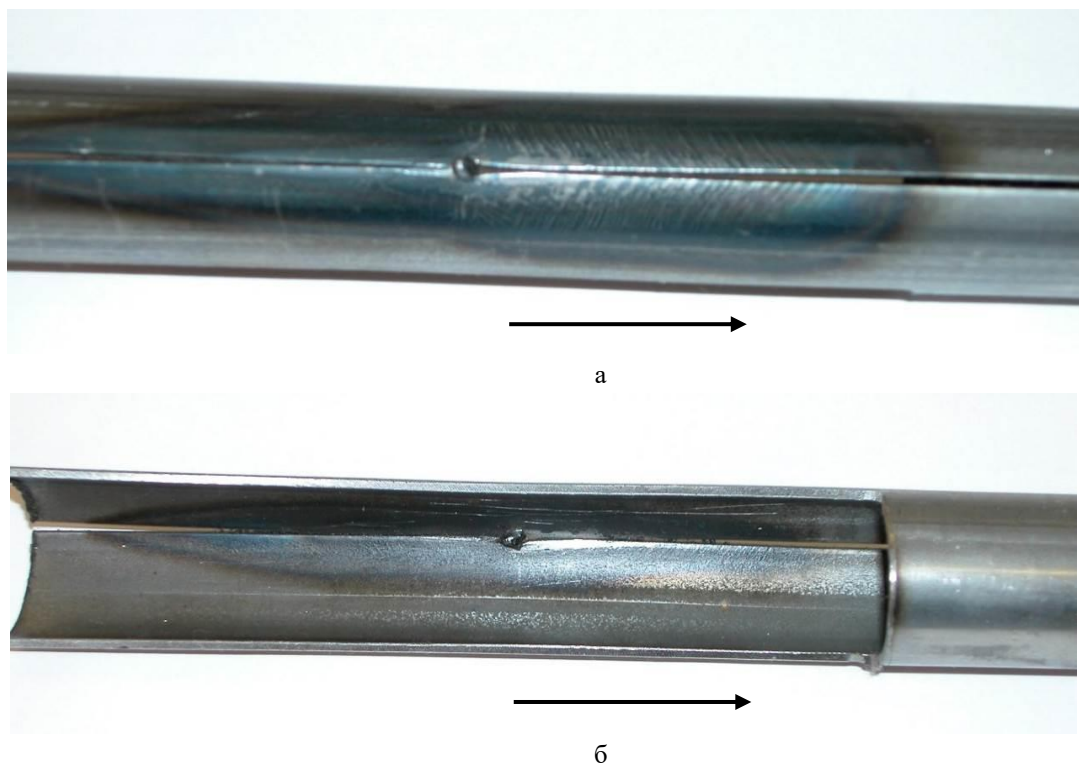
Выплеск в зоне сварки шва на внешней (а) и внутренней (б) стороне трубной заготовки при стационарном положении индуктора.
